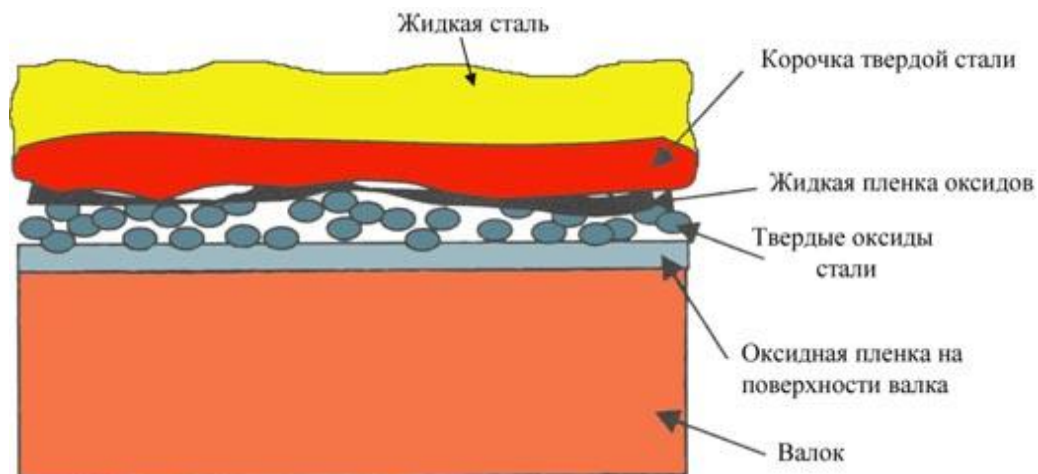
Схематичне представлення процесу твердіння твердої кірочки сталі на валку
